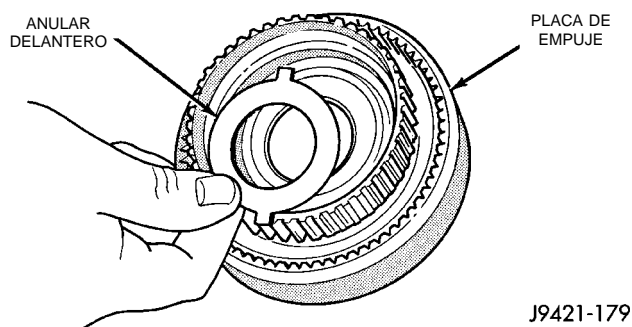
Emplazamiento de la placa de empuje en el soporte del engranaje anular delantero
